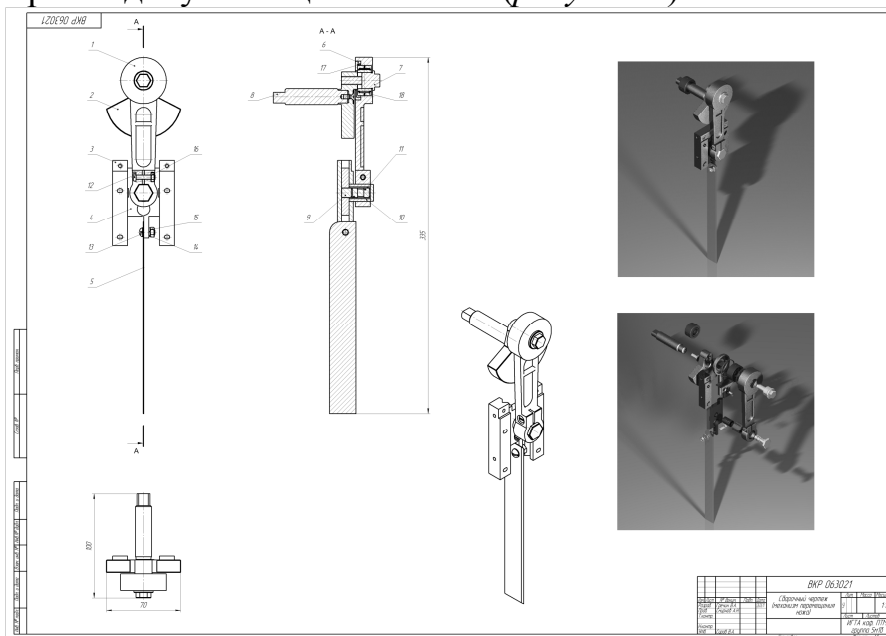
Рабочий чертеж механизма передвижения ножа машины «ЭЗМ-2»
